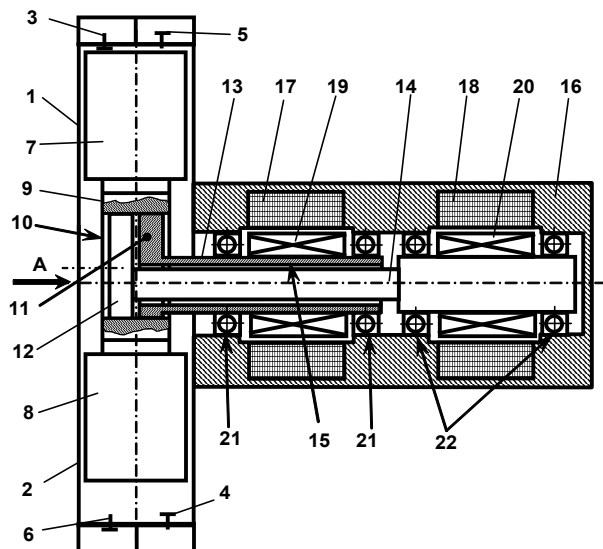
Схема продольного сечения конструкции оппозитного компрессора с совмещенными электродвигателями
